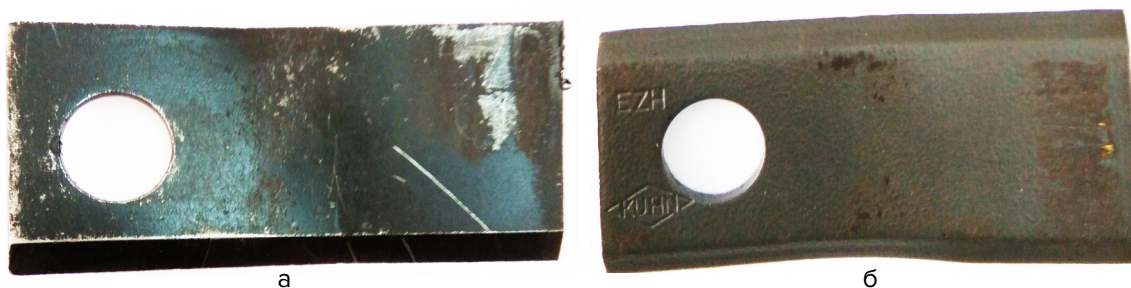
Внешний вид ножей после изгибающей нагрузки 25 кН:
